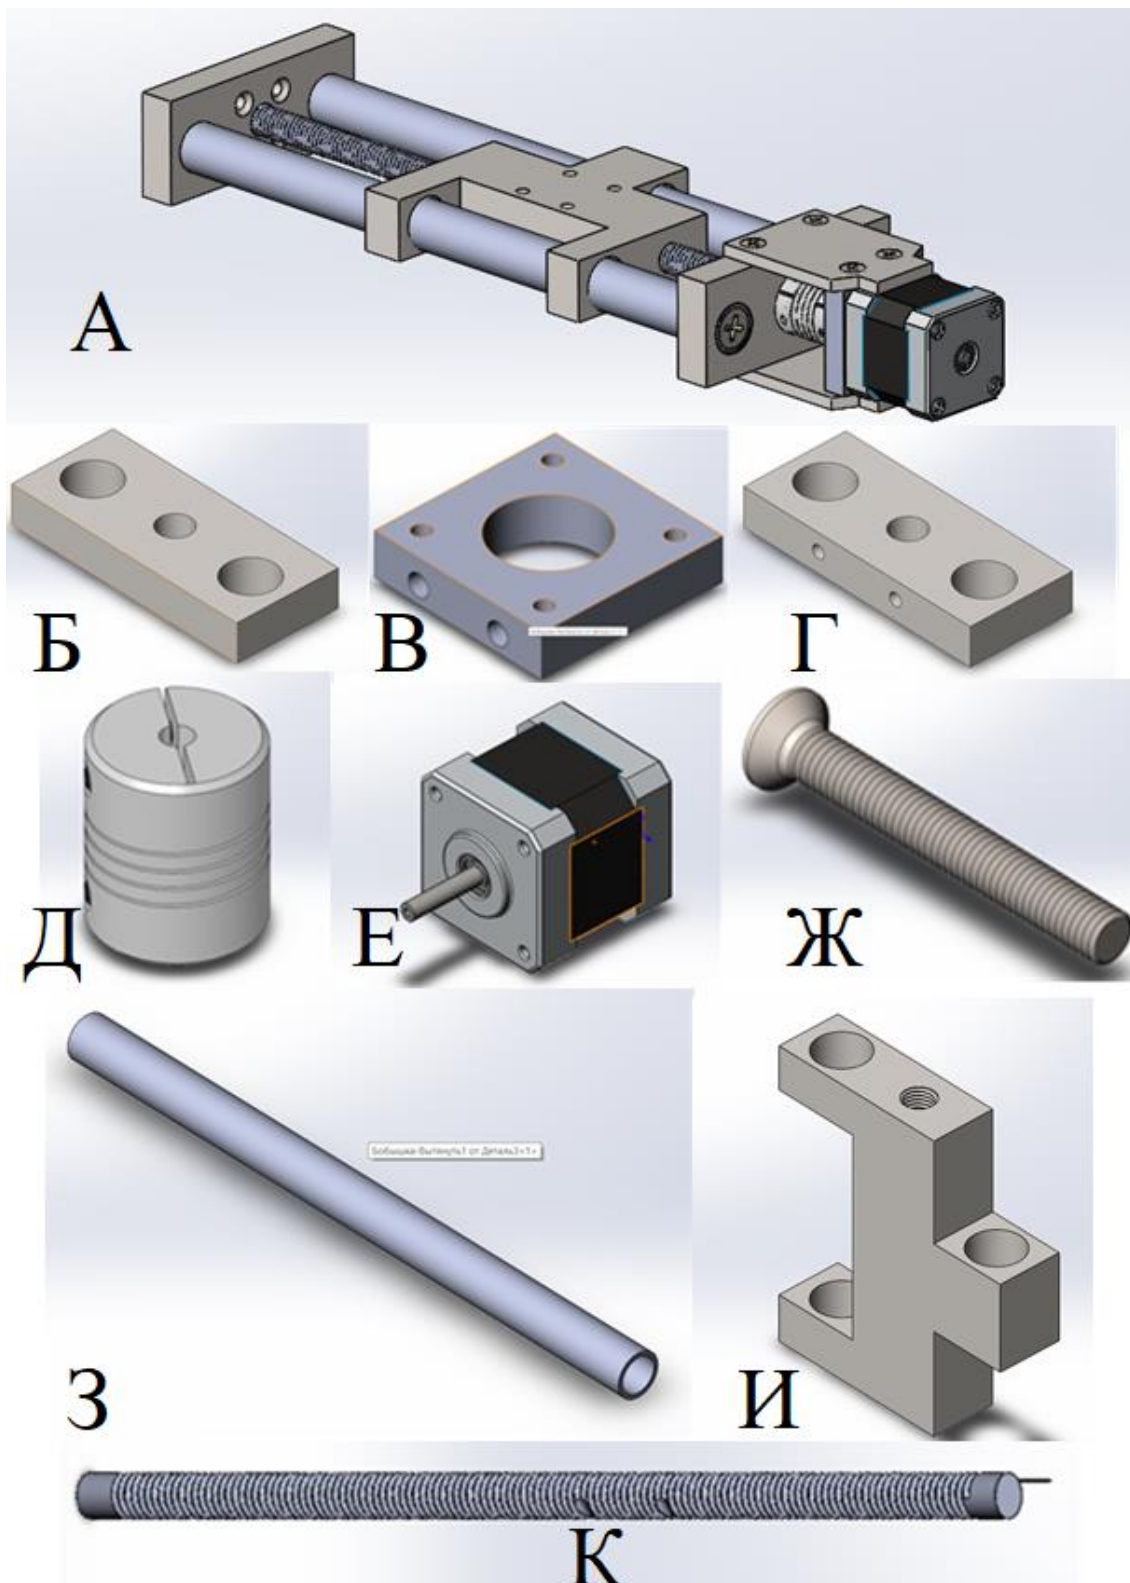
3D модели сборочных единиц робота манипулятора: А – Звено робота манипулятора; Б – Упорная стенка; В – Крепление двигателя; Г – Упорная стенка; Д – Муфта; Е – Двигатель; Ж – Винт с головкой с крестообразным шлицем 35x5 мм; З – Направляющая; И – Каретка; К – Винт
